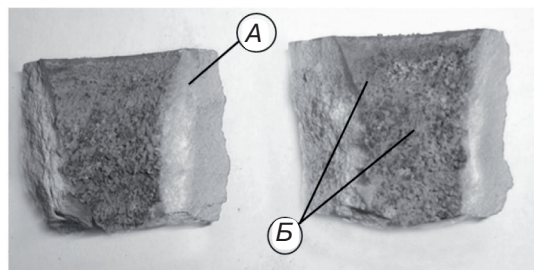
Фрагменты «калибровочной» вставки стакана-дозатора с отложениями неметаллических включений: поз. А – тело «калибровочной» вставки; поз. Б – отложения неметаллических включений
